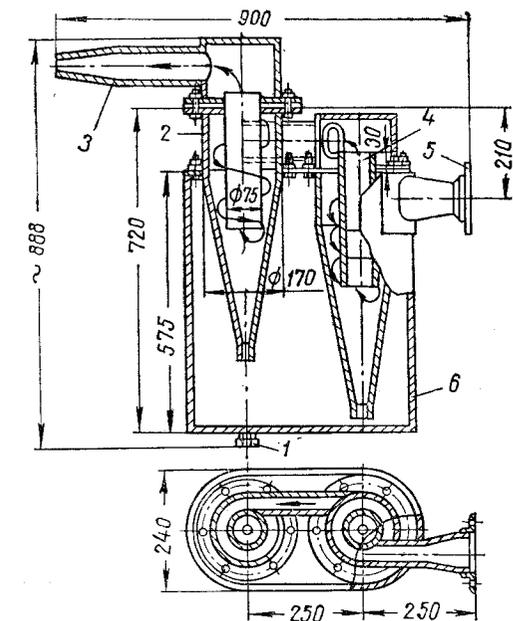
Маслоотделитель системы выхлопа: 1 — пробка отверстия сливного; 2 — циклон; 3 — насадка коническая; 4 — труба; 5 — фланец; 6 — корпус
